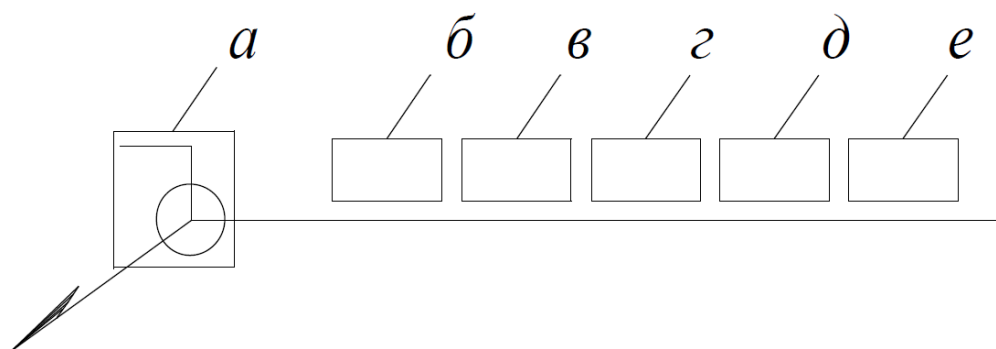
Схема структурного обозначения сварного шва:
